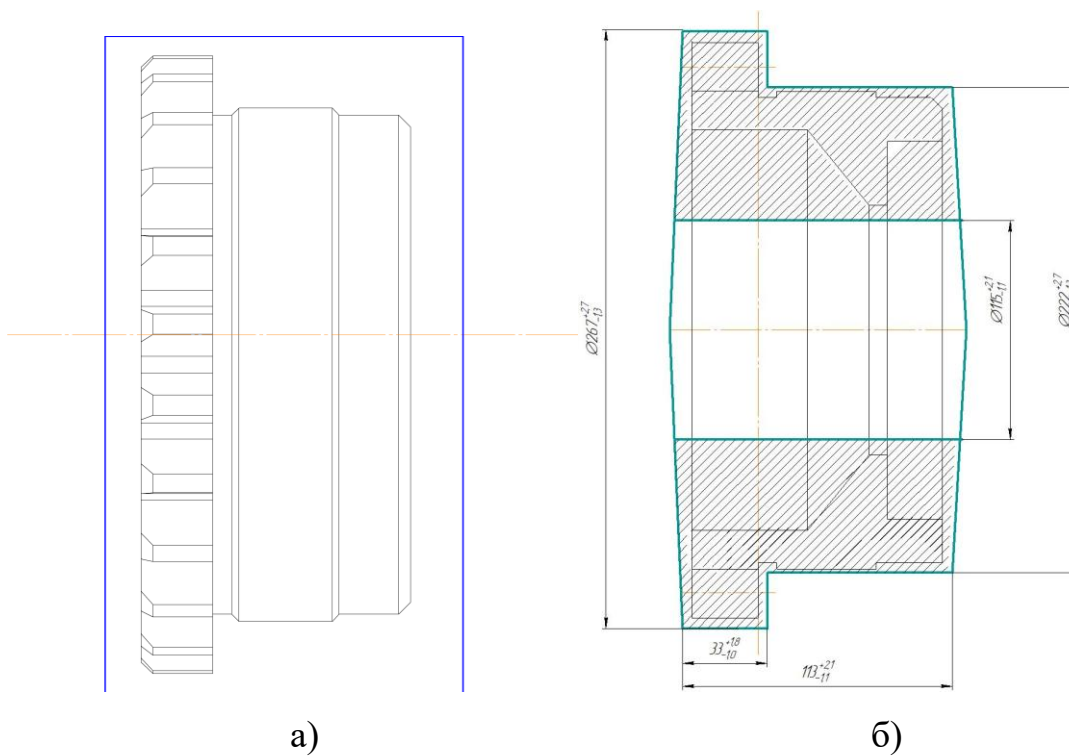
Ескізи заготовок: а) заготовка з прокату;
